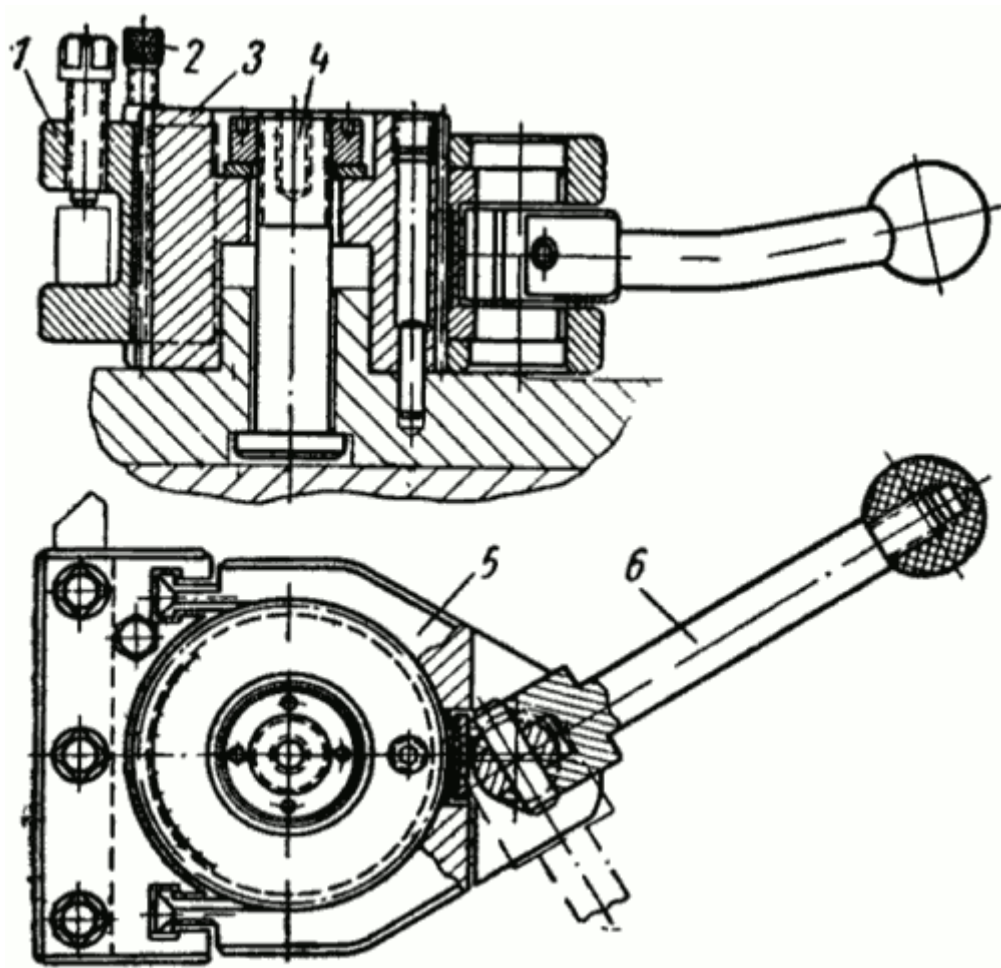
Приспособление для круглого наружного и внутреннего шлифования на токарном станке
